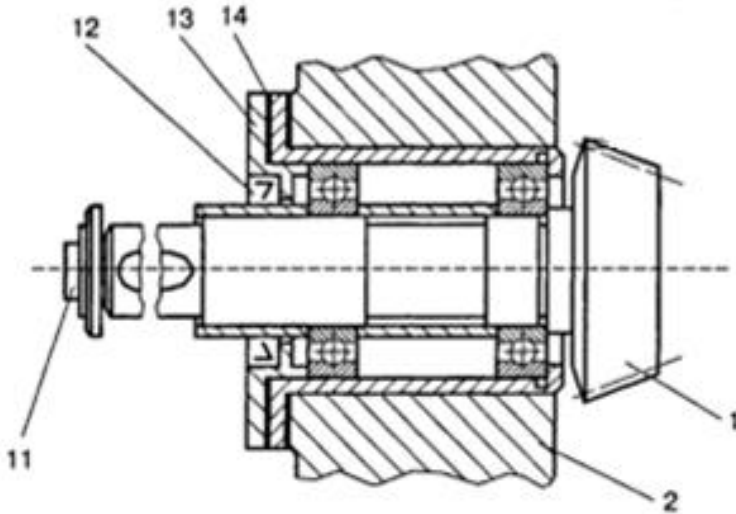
Збиральна одиниця: 1 – вал – шестерня; 2 – корпус;
